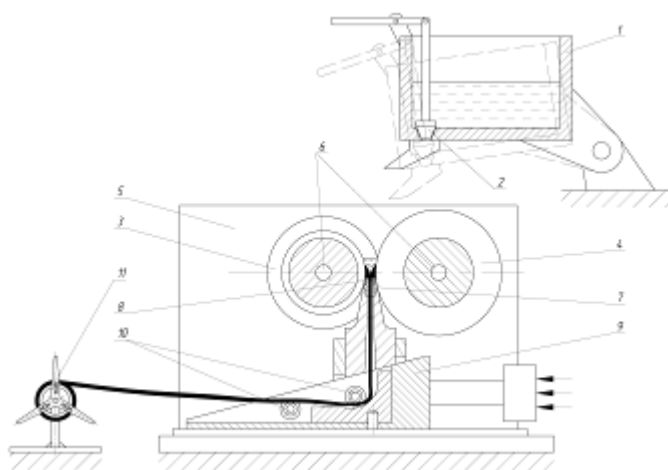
Устройство для непрерывного литья, прокатки, прессования по патенту № 73245:
